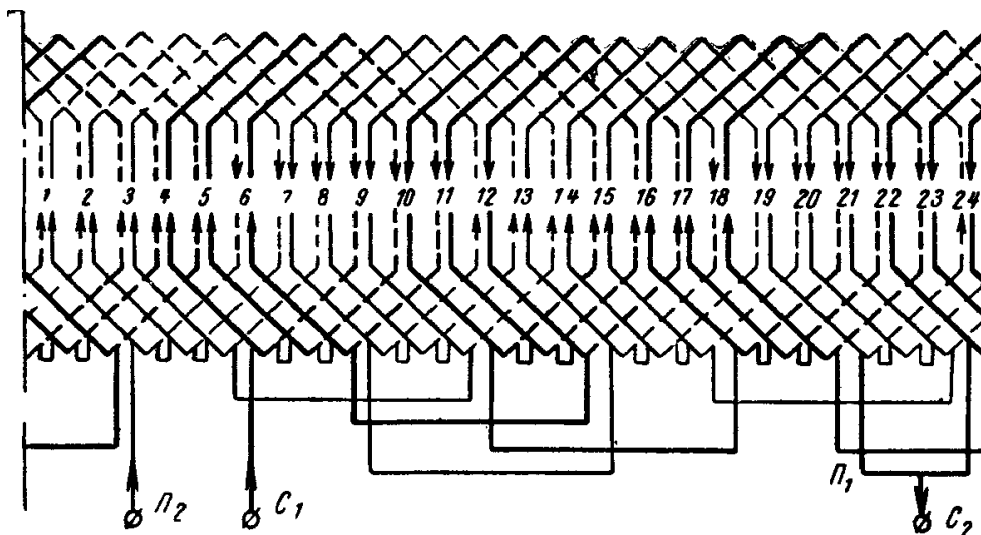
Схема двухслойной обмотки однофазного конденсаторного двигателя.
